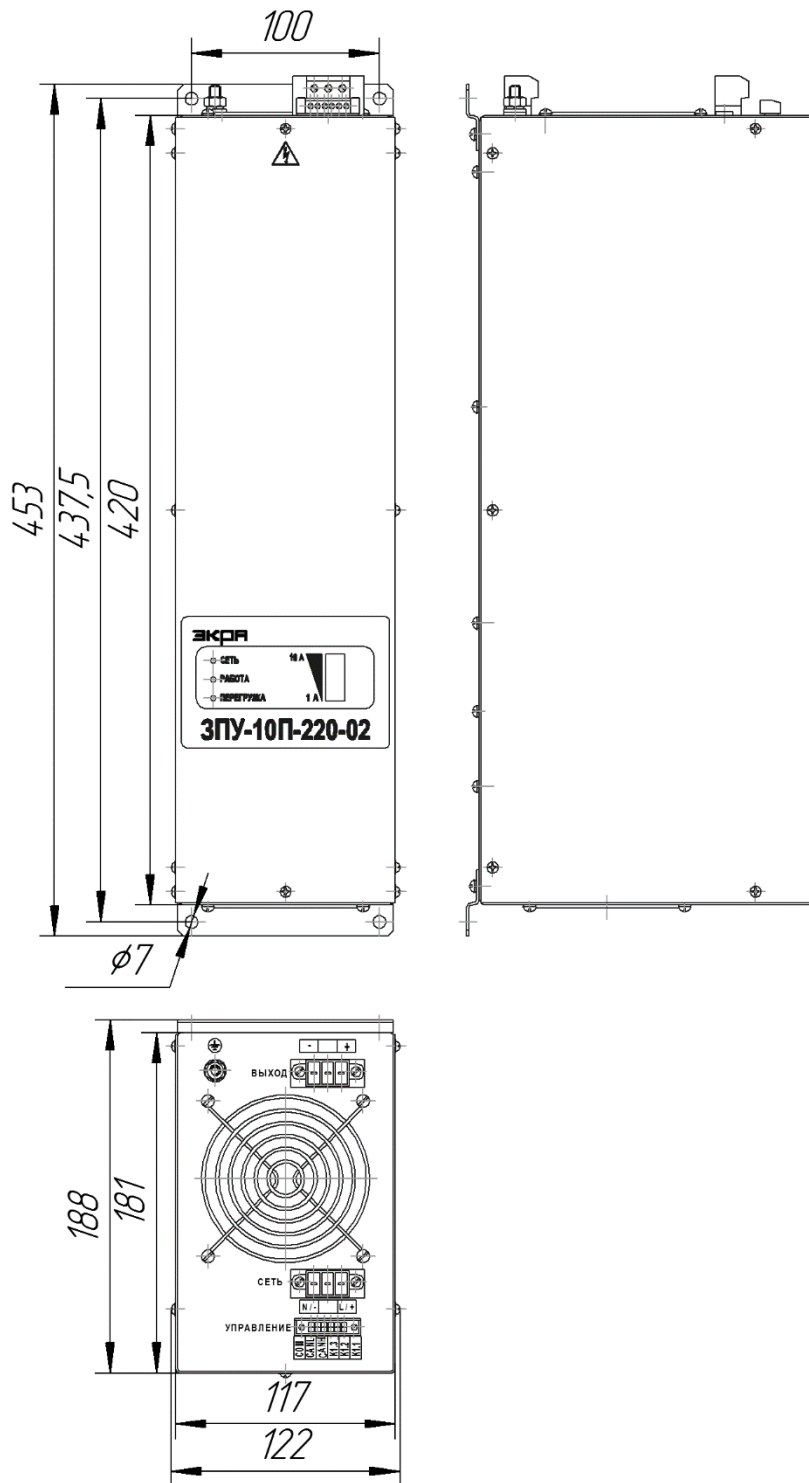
Габаритные и установочные размеры модуля питания
